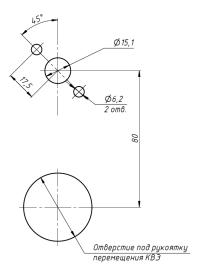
Установочные размеры рукоятки на фасаде КРУ (вид с фасада)
